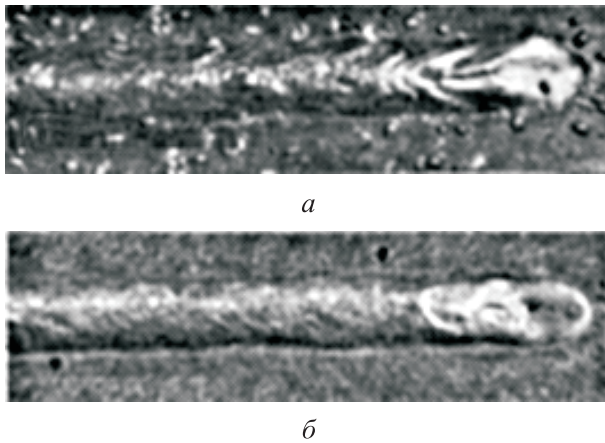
Внешний вид валиков, наплавленных под водой на глубине 90 м сварочной горелкой с ВЗ в аргоне при расходе защитного газа $G_r = 50$ л/мин, расходе воды $G_b = 8$ л/мин, напряжении $U = 40$ В, скорости сварки $v = 18$ м/ч, силе тока $I = 250$ (а) и 300 А (б)
